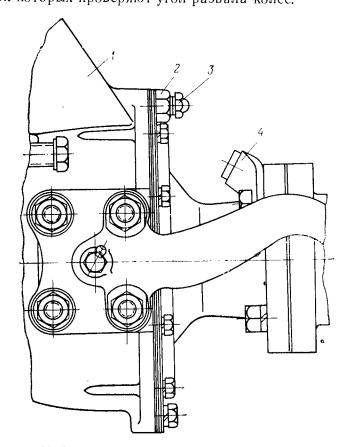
Установка упора-ограничителя поворота колес автомобиля УАЗ-452:
